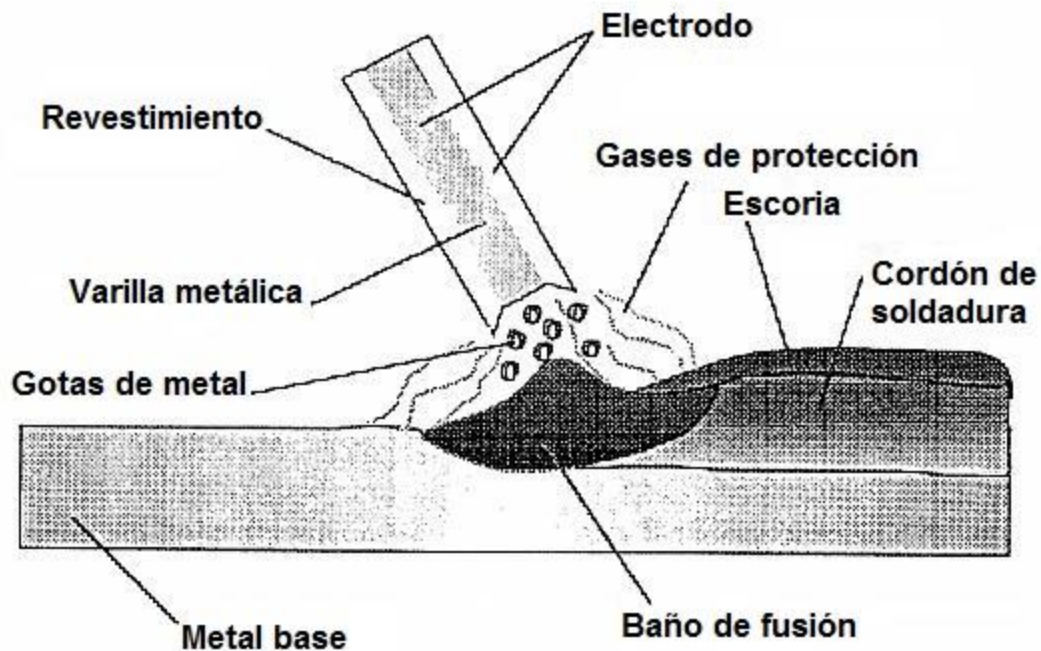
Soldadura de arco metálico con electrodo revestido.
